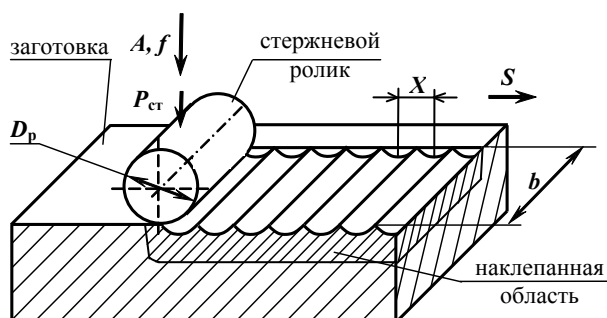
Схема нанесения отпечатков на плоскую поверхность заготовки стержневым роликом при статико-импульсной обработке
